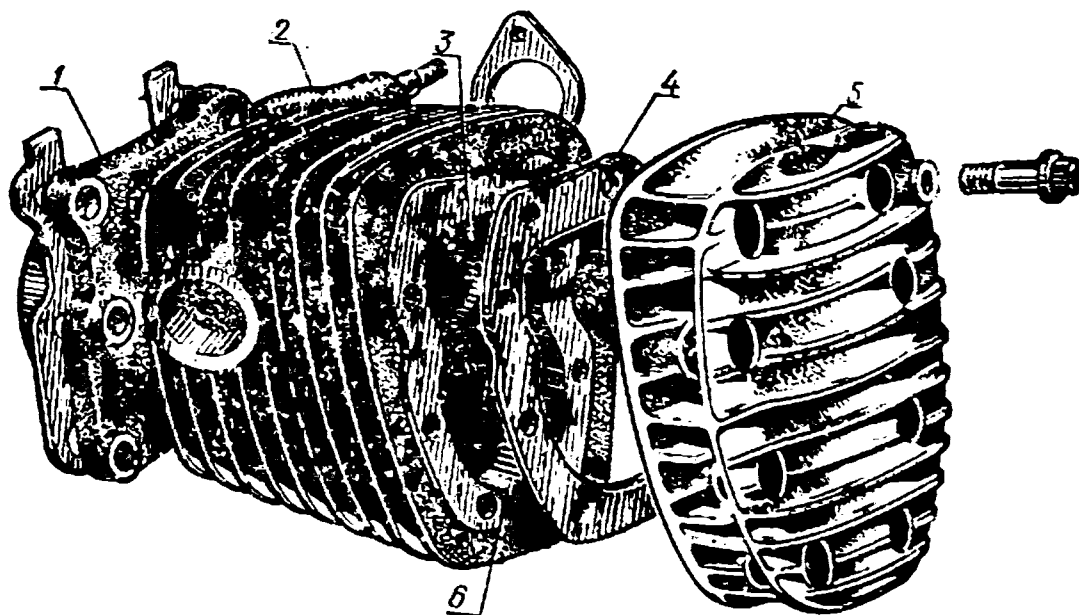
Цилиндр, прокладка и головка цилиндра четырехтактного двигателя с нижними клапанами:
